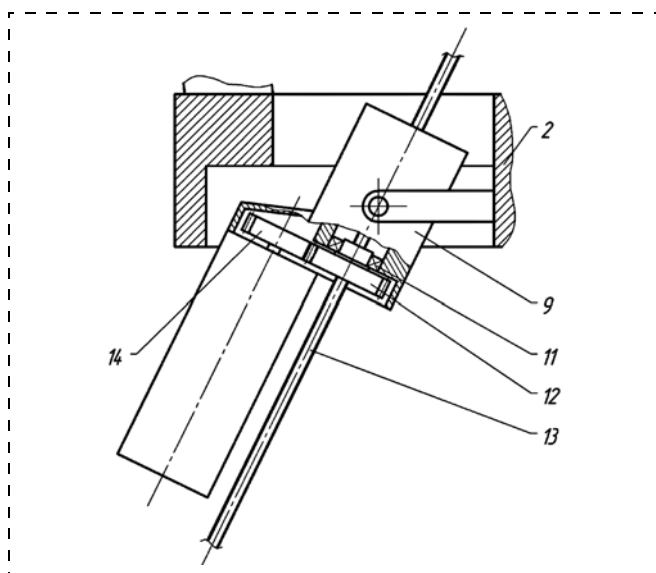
Привод автономного перемещения секции ПНП: 11 — подшипник; 12 — зубчатое колесо; 13 — ходовой винт; 14 — шестерня
